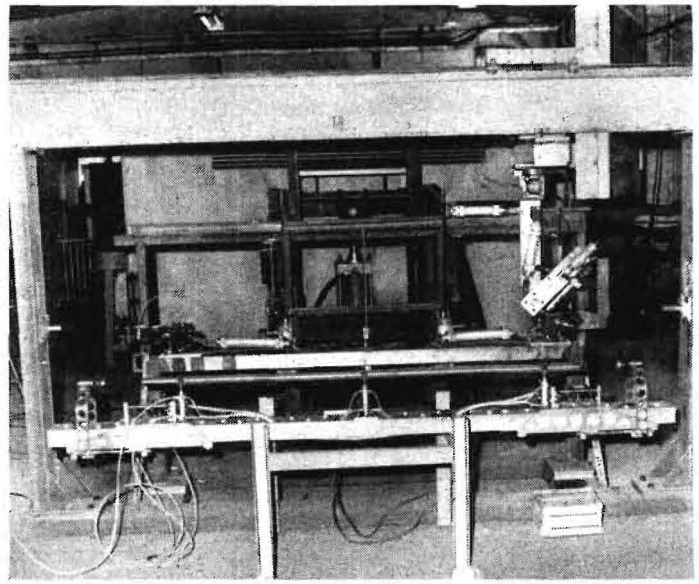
Schweißanlage für Rohre und Laschen
